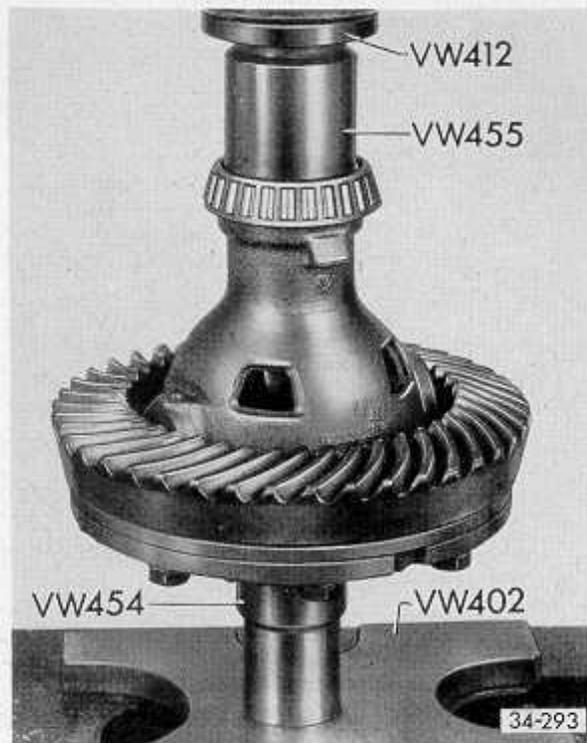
Innenring/Kegelrollenlager auf ca. 100° C erwärmen, aufsetzen und nachpressen.
